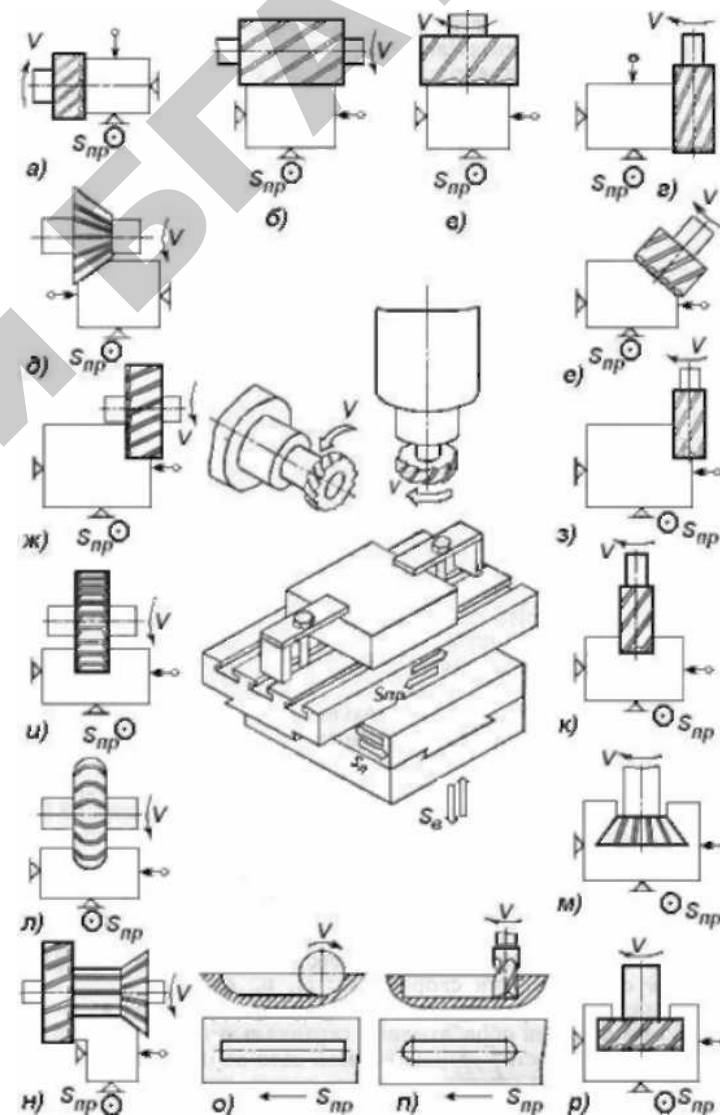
Типы фрез и схемы обработки поверхностей на фрезерных станках
